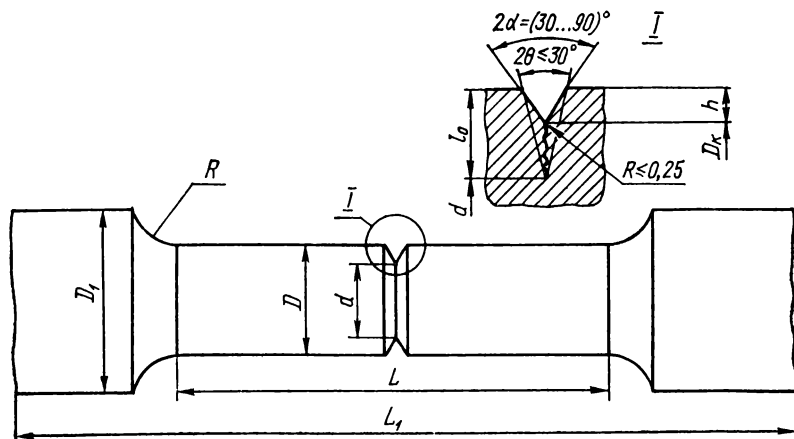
Цилиндрический образец для испытаний на растяжение или изгиб:
